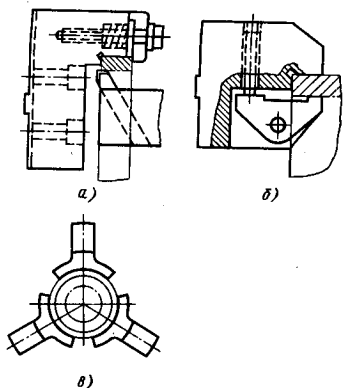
Наладки кулачков для закрепления тонкостенных заготовок: а - по торцам; б - с двусторонним сжатием; в - по поверхности с большой дугой охвата
